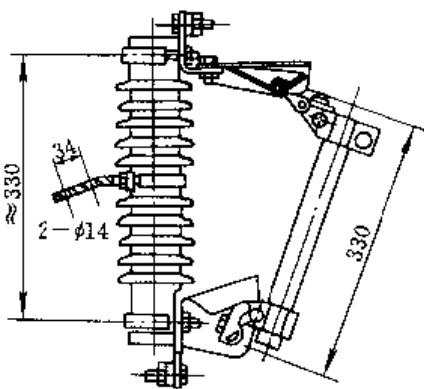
RW7—10 型户外高压跌落式熔断器外形尺寸
